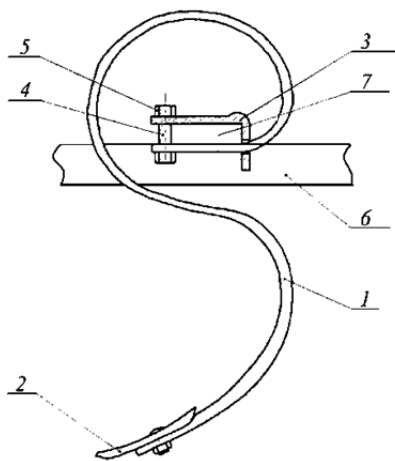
Крепление рыхлительной лапы: 1 — стойка; 2 — наральныйник; 3 — зажим; 4 — болт; 5 — гайка; 6 — рамка; 7 — планка [3, с. 20]
